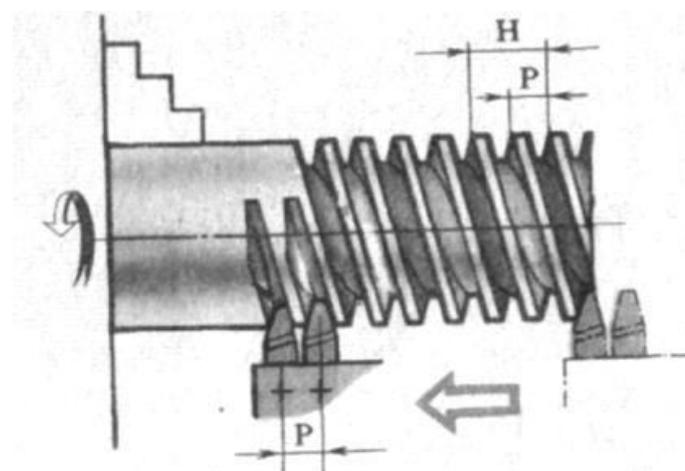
Схема нарезания двухзаходной резьбы двумя резцами
